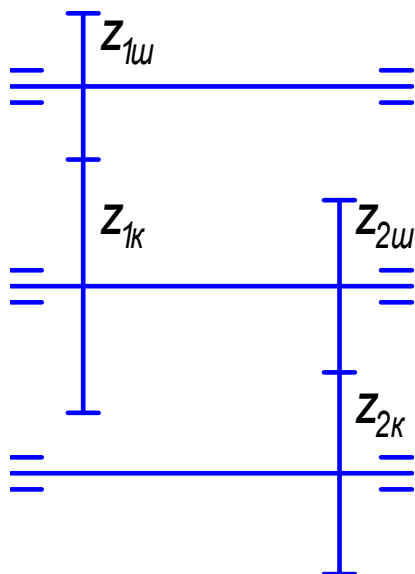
Кінематична схема двоступінчастого циліндричного редуктора
